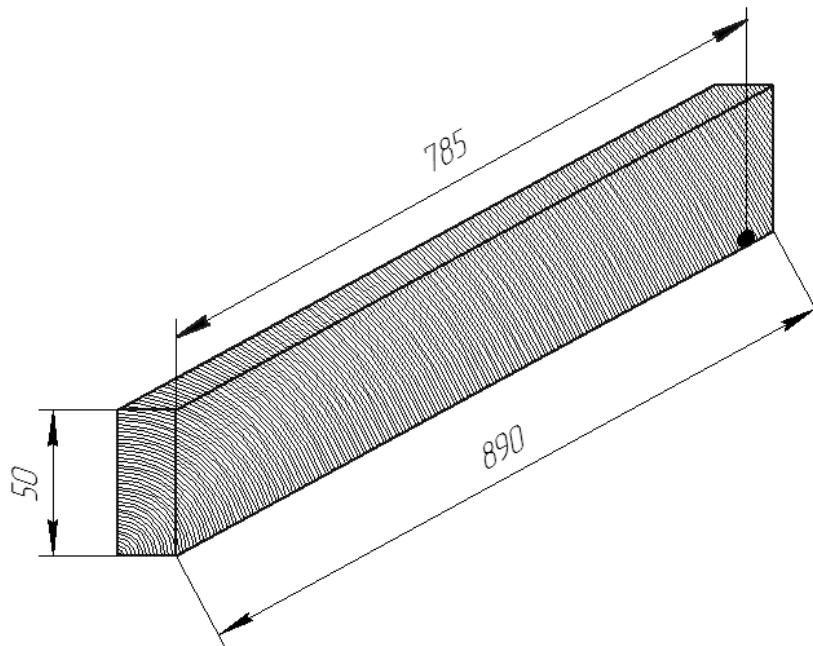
Продольный рез заготовки. Диаметр сучка 20 мм
